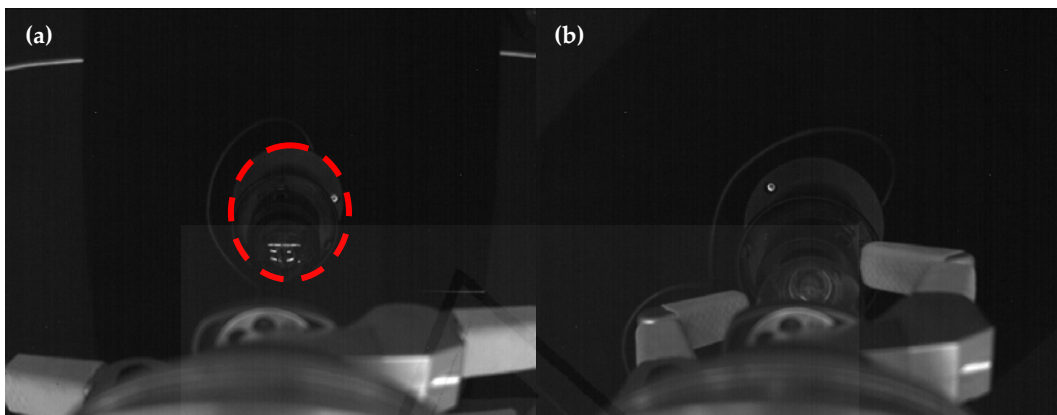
(a) Posición en la que se ejecuta control visual virtual para obtener la posición relativa entre la bombilla y la cámara (b) Posición de agarre de la bombilla en la lámpara
